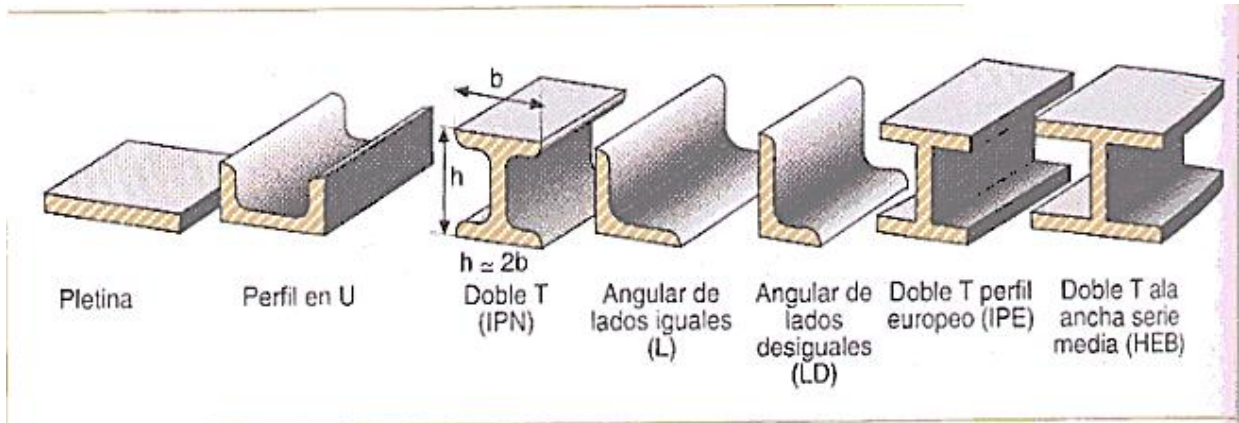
Perfiles estructurales obtenidos mediante laminado
